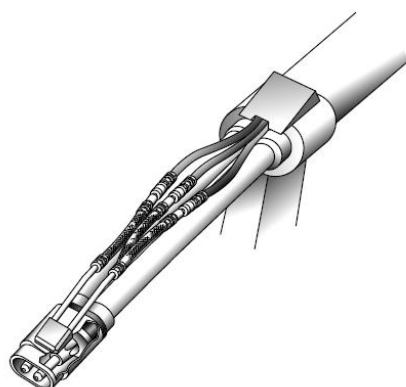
Головка для сварки двумя проволоками
